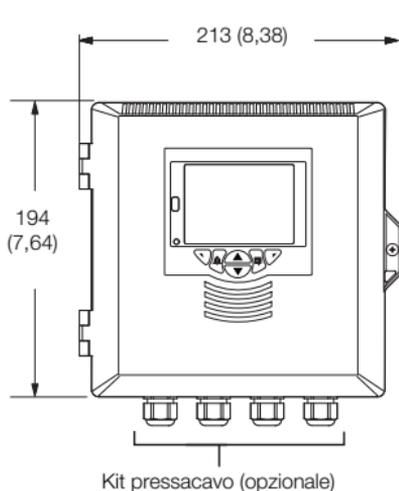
ControlMaster CMF160 per montaggio su pannello
